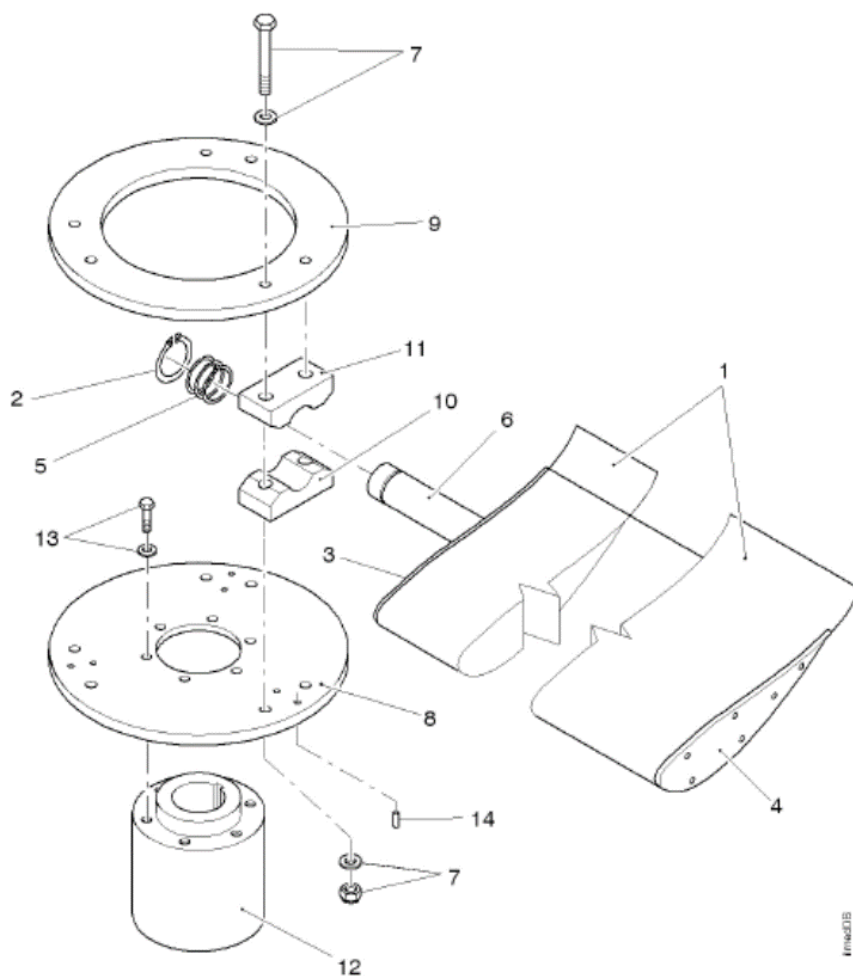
Основные компоненты однодискового рабочего колеса вентилятора
